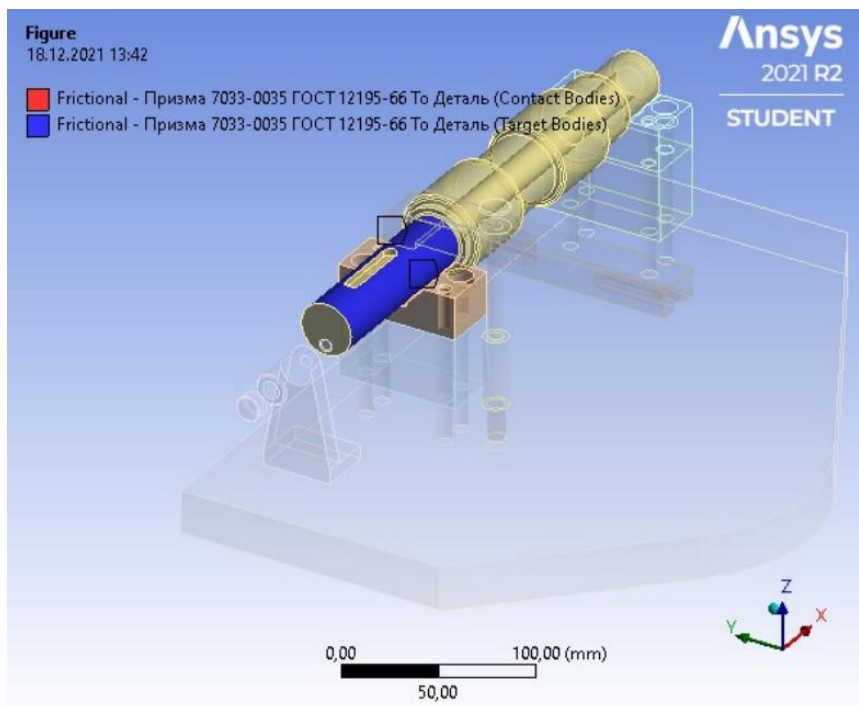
Сполучення між поверхнею заготовки та передньою призмою
